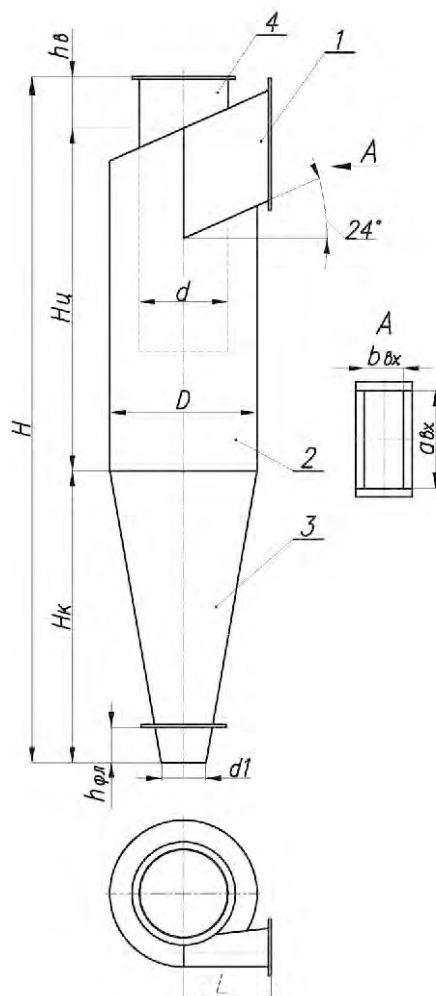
Общий вид. Габаритные и присоединительные размеры ЦН-24.
